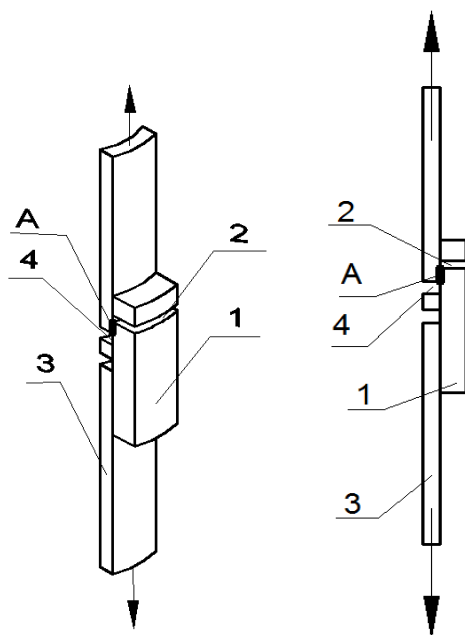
Образец для определения прочности раструбного сварного соединения
